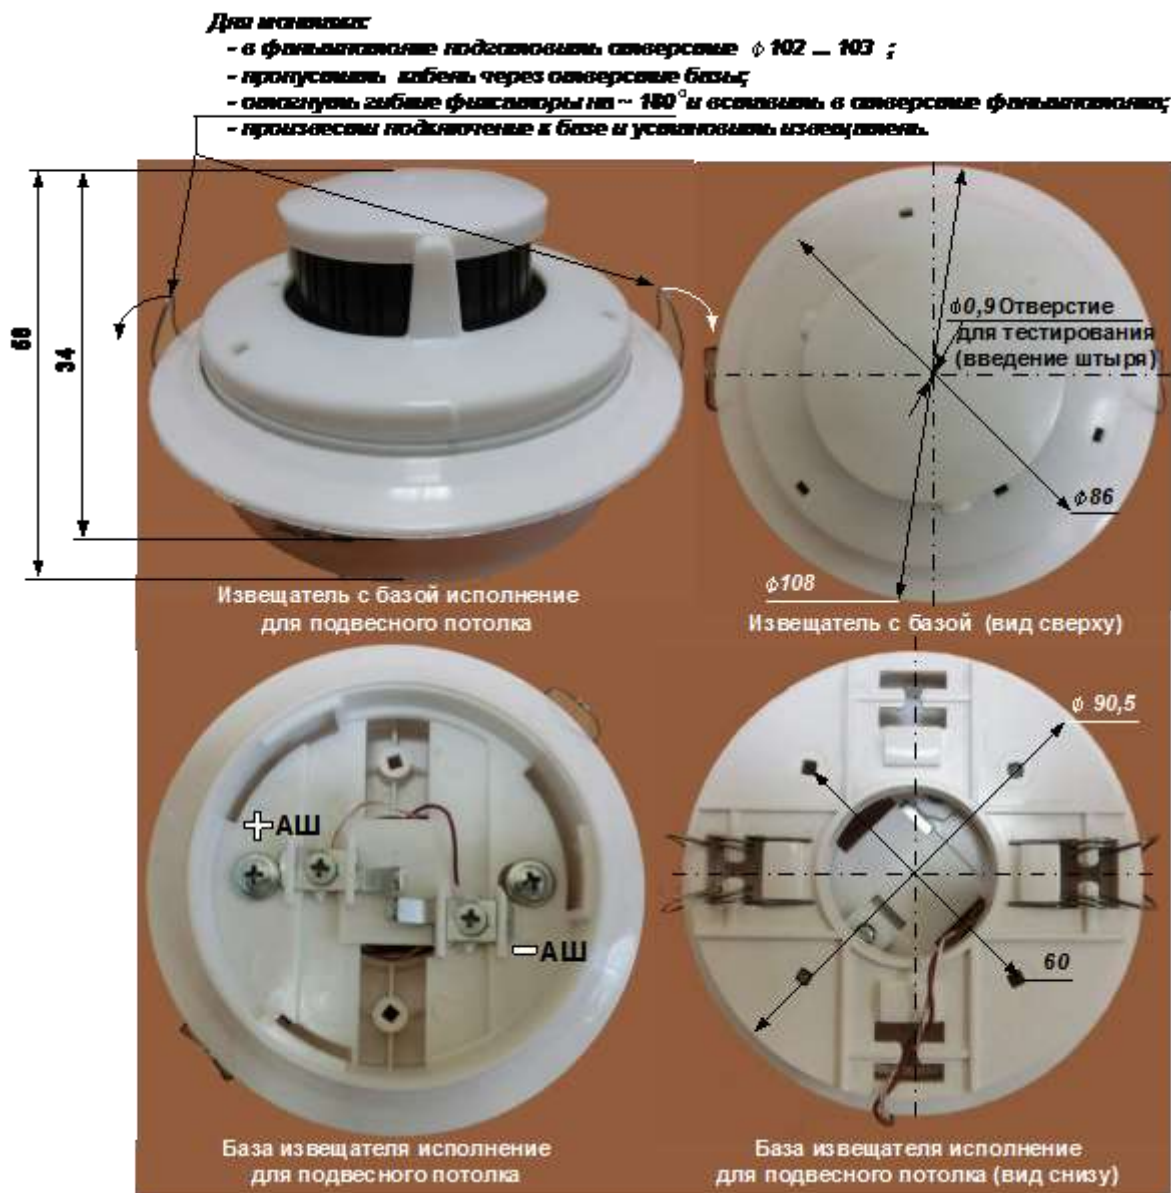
АЗДПИ. Извещатель с базой для подвесного потолка. Габаритные и присоединительные размеры.
